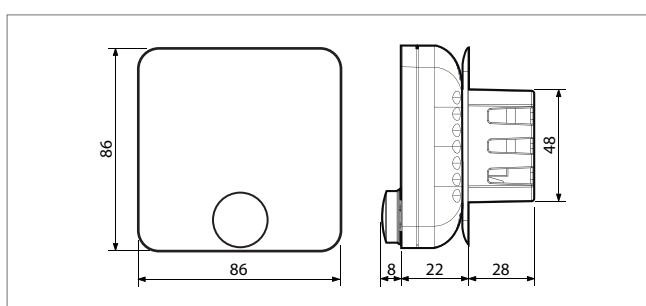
Dimenzijski crtež upravljačkog terminala zone za ugradnu montažu (dimenzije u mm)
